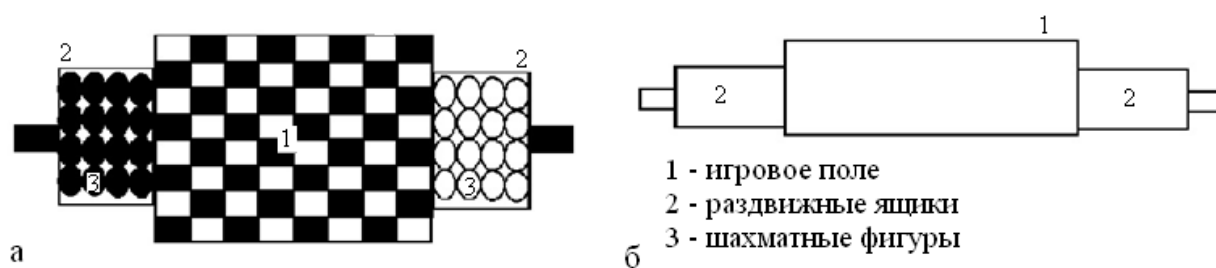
Конструкция шахматной доски: а – вид сверху; б – вид сбоку
